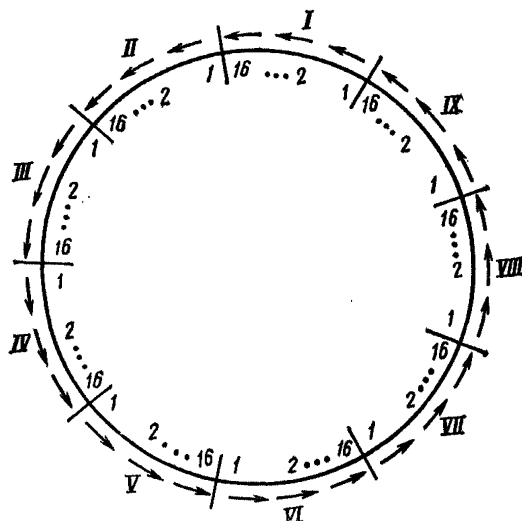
Схемы сварки кольцевых швов, соединяющих корпус с дном:
